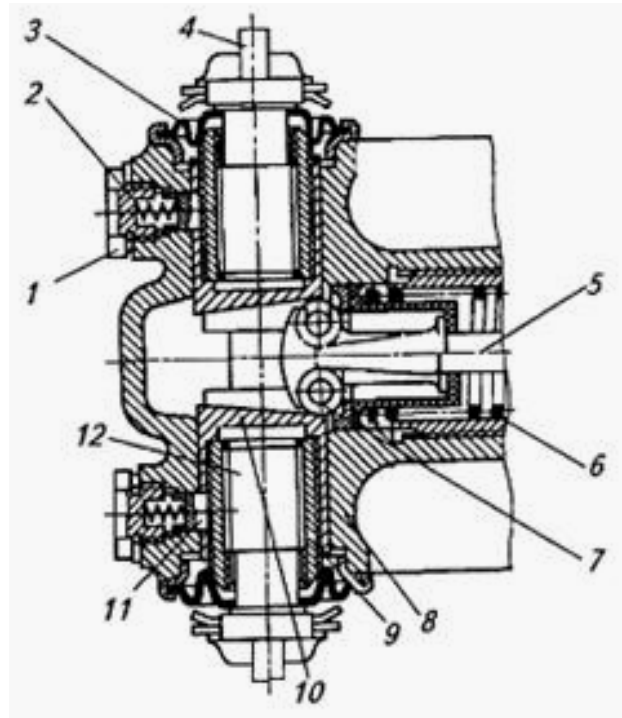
Клиновое разжимное устройство автомобиля КАЗ-4540 с автоматической регулировкой зазора: 1 - пробка; 2 - пружина; 3 - грязезащитный колпак; 4 - тормозная колодка; 5 - клин; 6 - пружина; 7 - ролик; 8 - суппорт; 9 - регулировочная втулка; 10 - толкатель; 11 - штифт храповик; 12 - регулировочный винт
